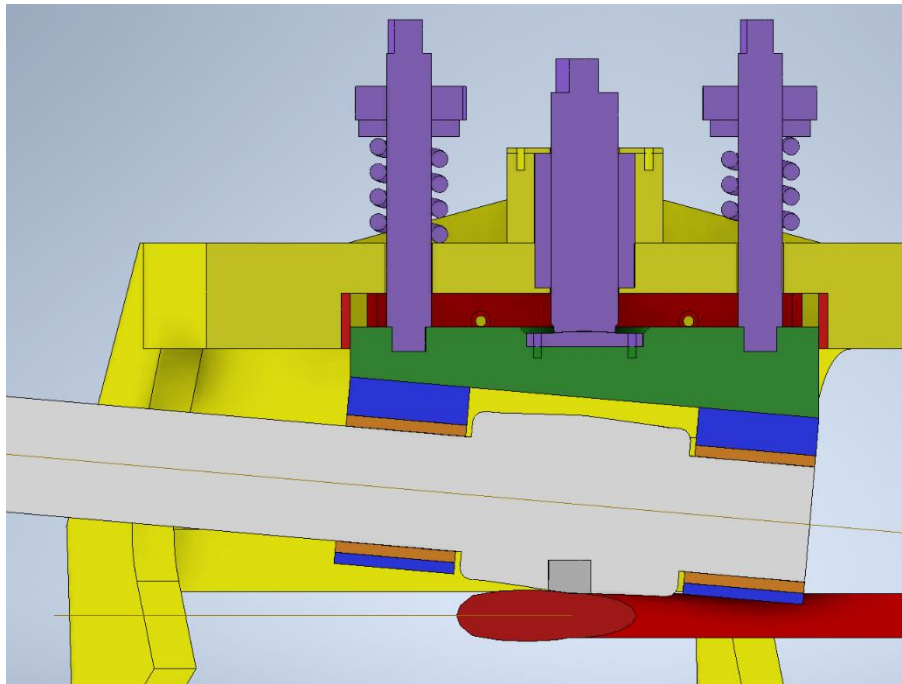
Продольный разрез конструкции валкового узла.
